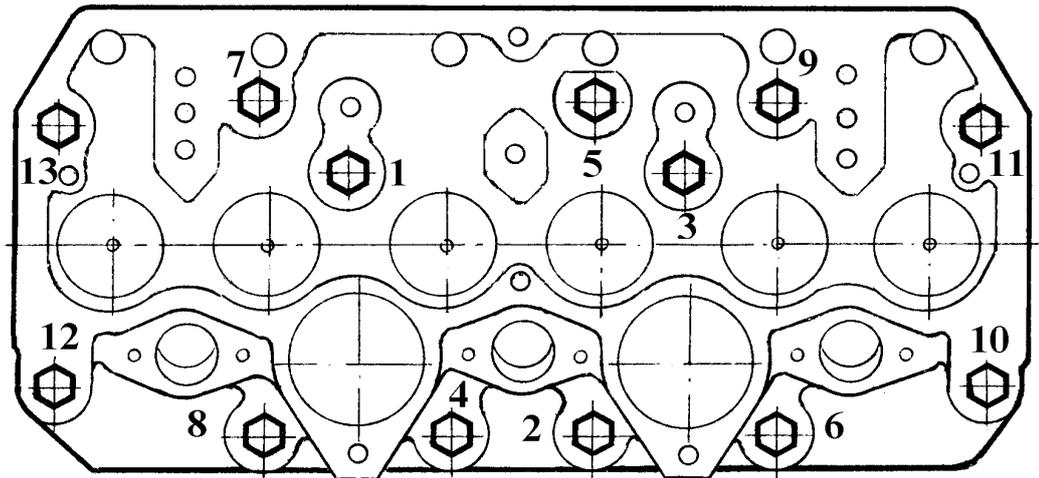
Схема последовательности затяжки болтов крепления головки цилиндров
